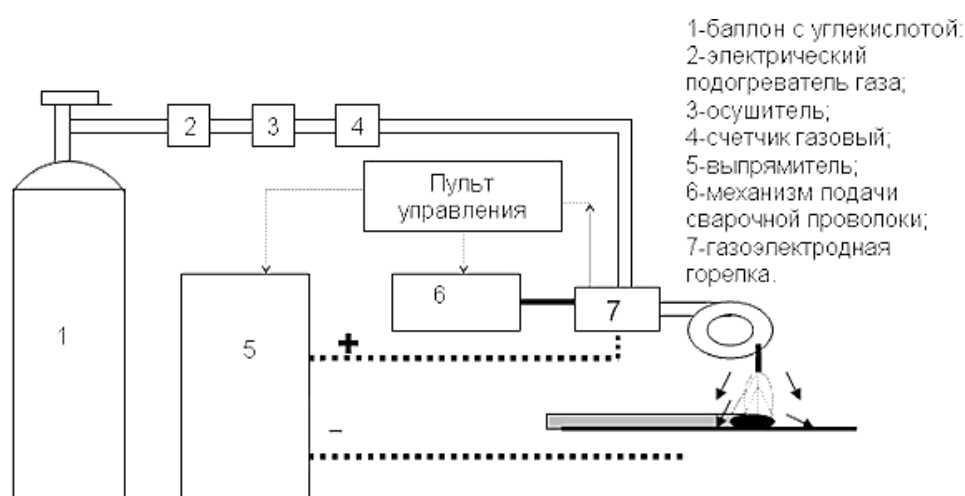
Схема установки для сварки в среде углекислого газа [7]
